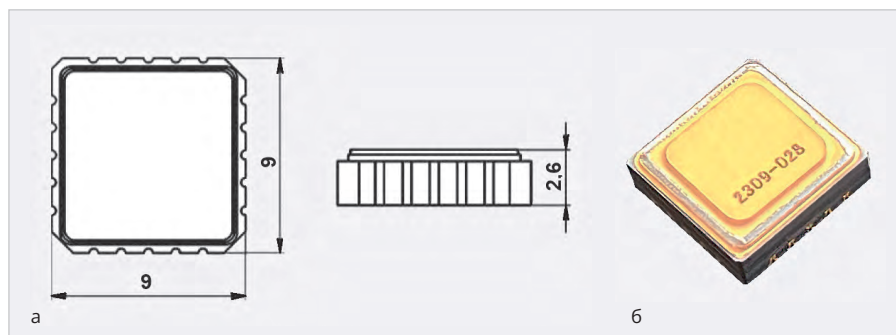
ИМС акселерометров: а) габаритные размеры; б) внешний вид
